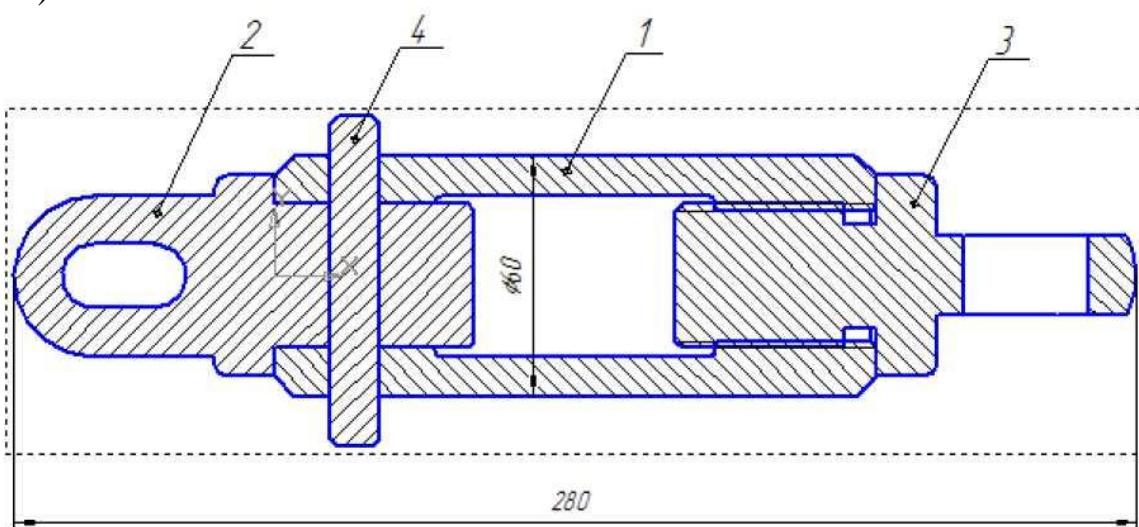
Простановка позиций на сборочном чертеже
